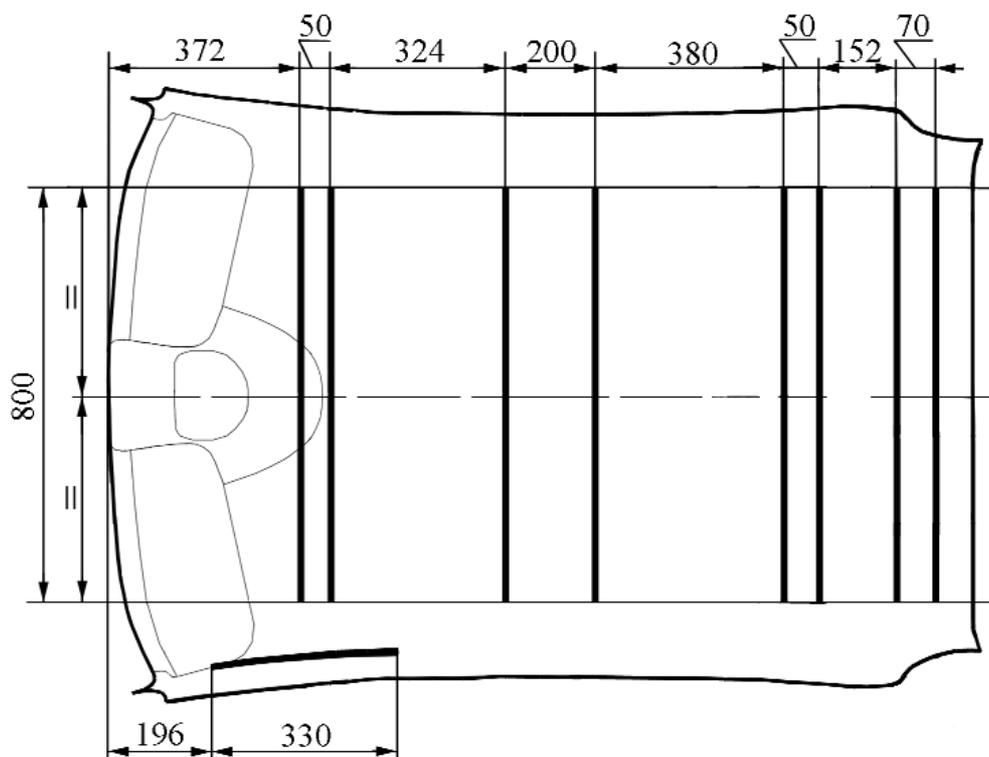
Схема нанесения клея на обивку крыши.
